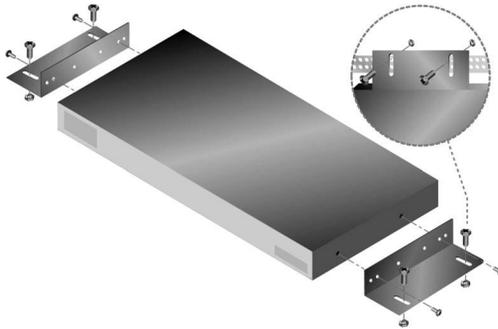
Vertikale Installation des Rack Console Switches
